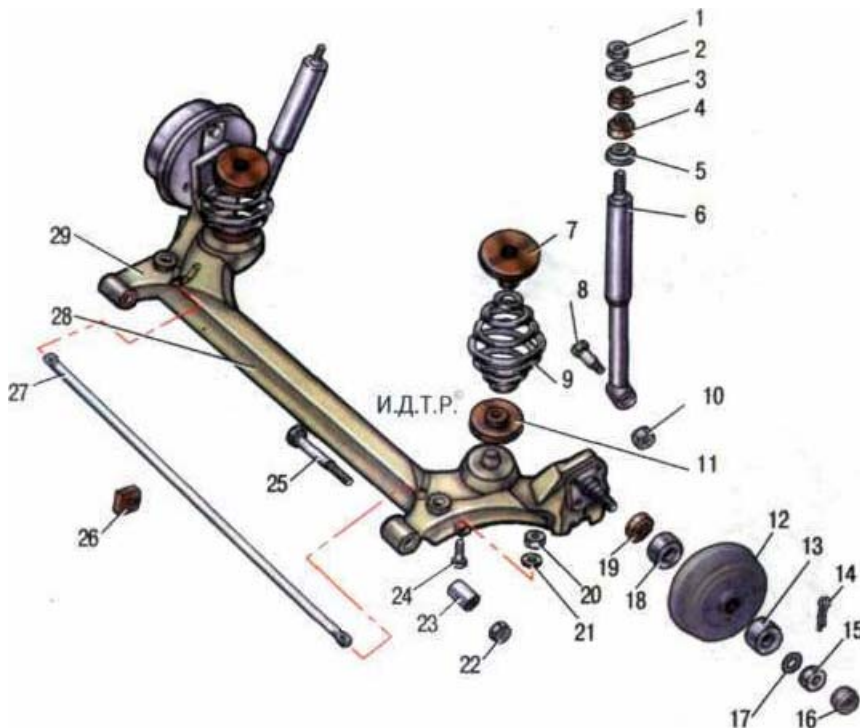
Задняя подвеска: 1 - гайка верхней опоры амортизатора; 2, 5, 21 - шайбы; 3, 4 - резиновые втулки; 6 - амортизатор; 7 - верхняя прокладка пружины; 8, 24, 25 - болты; 9 - пружина задней подвески; 10, 20, 22 - гайки; 11 - нижняя прокладка пружины; 12 - тормозной барабан; 13 - наружный подшипник; 14 - шплинт; 15 - гайка; 16 - защитный колпак; 17 - стопорная шайба; 18 - внутренний подшипник; 19 - сальник; 23 - сайлентблок; 26 - подушки стабилизатора; 27 - стабилизатор; 28 - балка задней подвески; 29 - рычаг подвески
